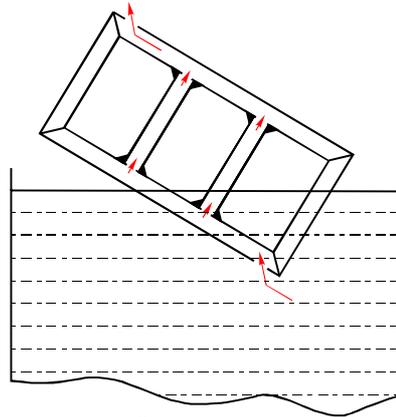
"Unsichtbare" Öffnungen an Rohrkonstruktionen
